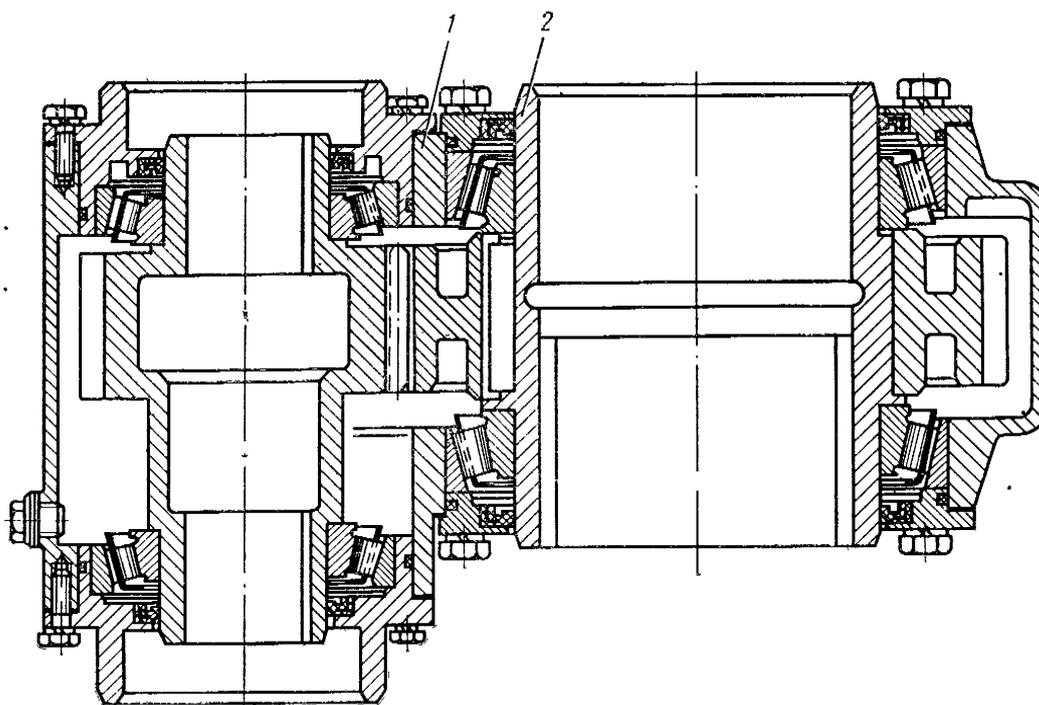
Поперечное сечение приводного механизма буровых установок моделей ПБУ, ЛБУ-50, ЛБУ-50-07, ЛБУ-50-08, ЛБУ-50-10, УБВ-318 (1- вал-шестерня для передачи крутящего момента на привод бурового устройства 2)
